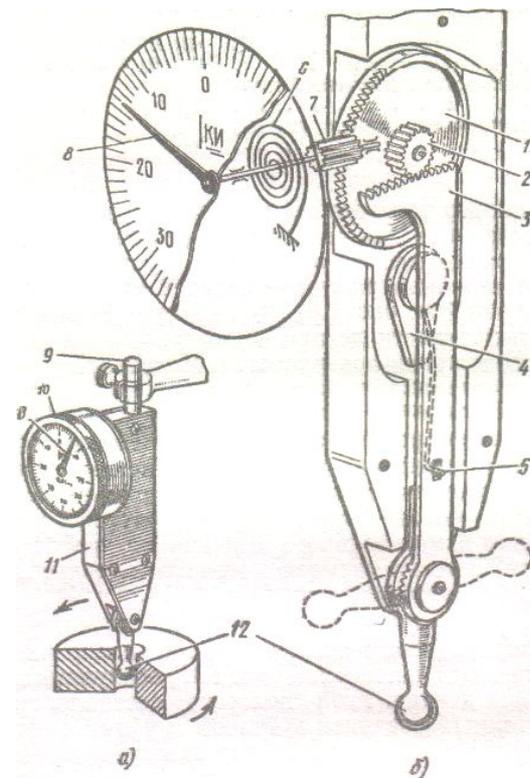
Индикатор ИРБ рычажно-зубчатый с боковой шкалой: а – общий вид; б – конструктивная схема
